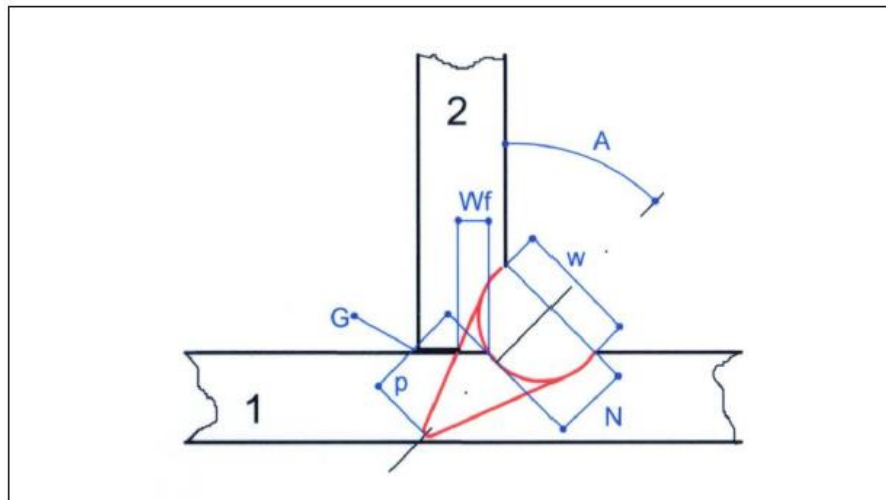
Soldadura de filete para soldadura láser. Observe la diferencia entre la penetración de soldadura (p) y el ancho de fusión W(f). Es la W(f) la que lleva la carga aplicada a la junta de soldadura y, por lo tanto, lo que debe especificarse. El relleno inferior (N) también es crítico y debe especificarse. Si el exceso (N) excede la "sensibilidad a la fisura" del material, la soldadura fallará.[3]
